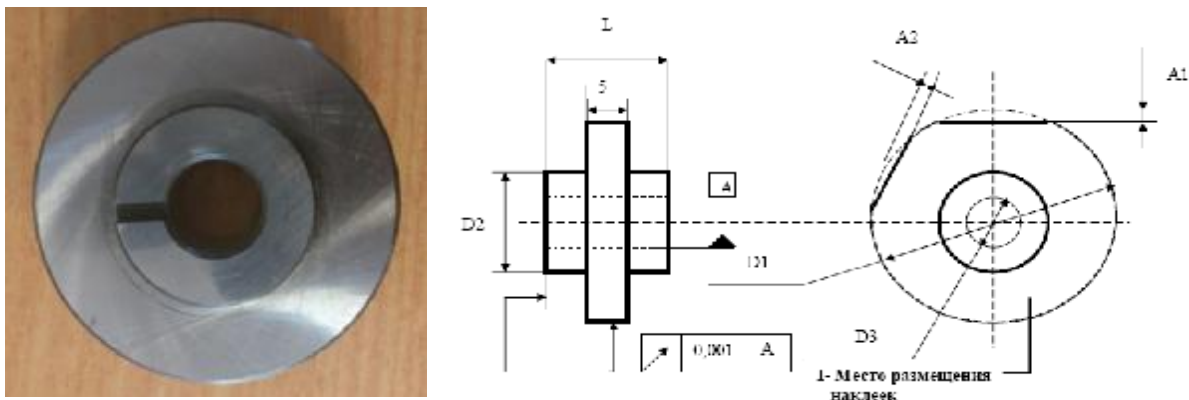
Внешний вид и эскиз мер для поверки межцентромеров
